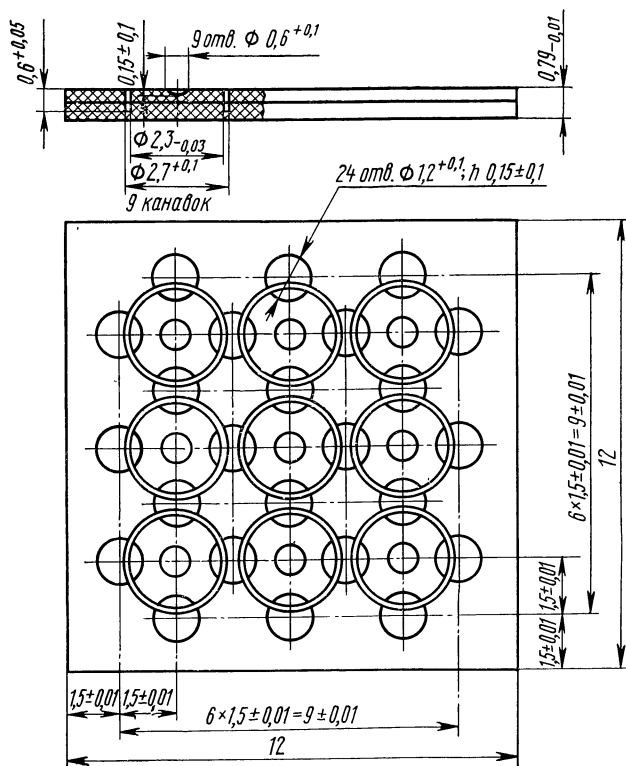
Групповая керамическая заготовка для девяти дисков и их элементы
